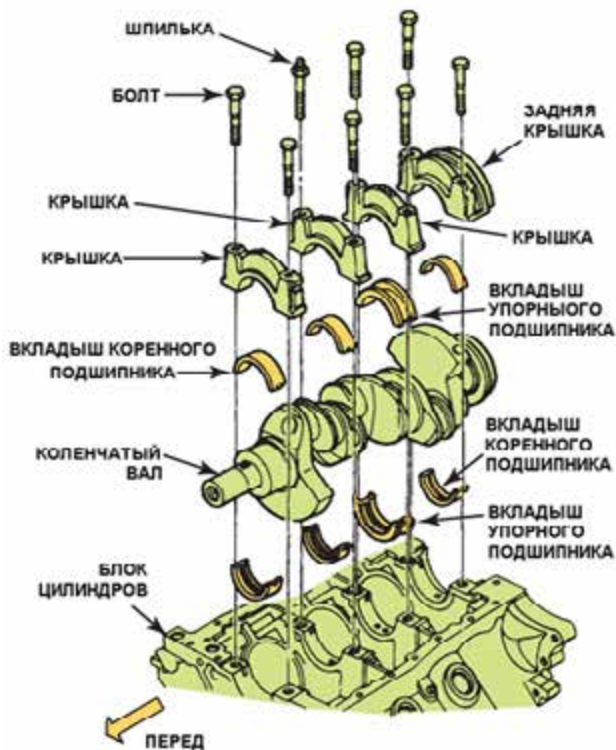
Коленчатый вал вращается в коренных подшипниках. Продольное перемещение коленчатого вала ограничивается упорным подшипником; источник: *Pearson Education, Inc.
